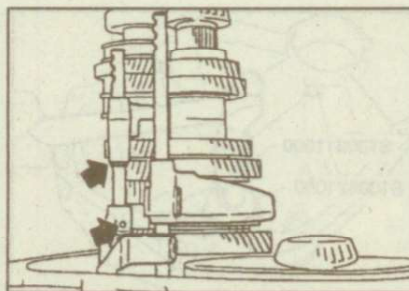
Установка вилки переключения 3-й и 4-й передач, стопорного кольца и штифта
